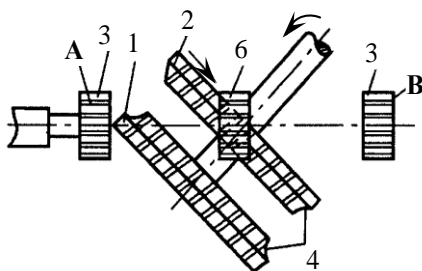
Схема обробки зубів циліндричних зубчастих коліс двома косокубними довбачами
